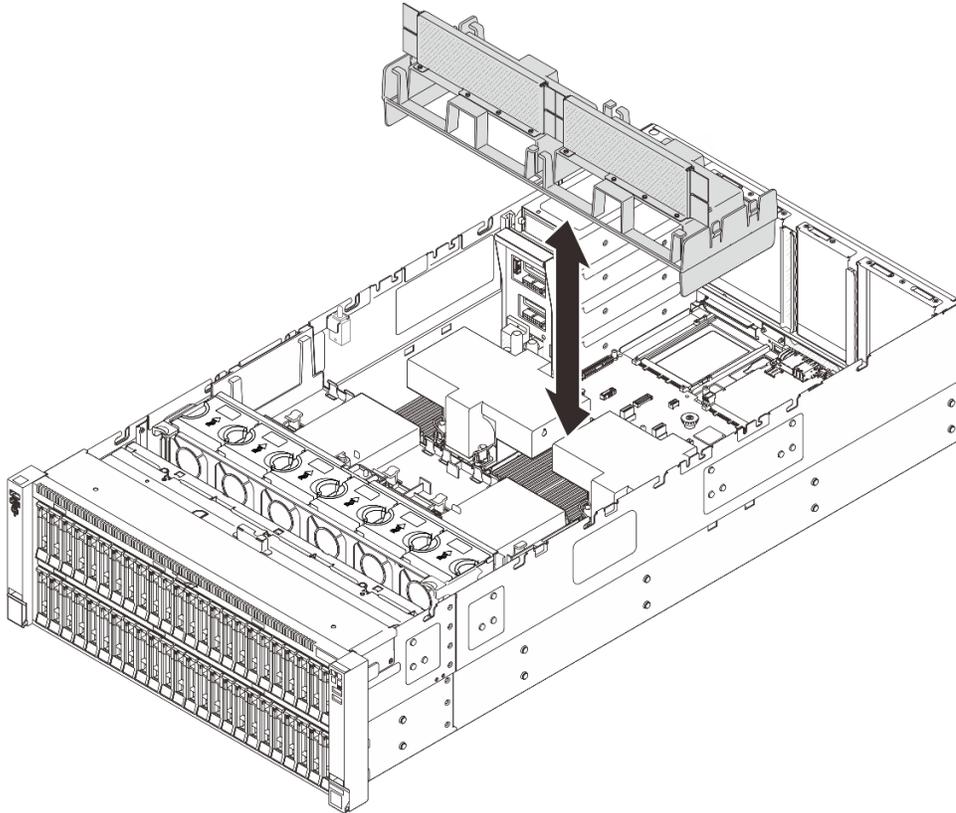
Retrait de la grille d'aération arrière pour un module de processeur-dissipateur thermique 2U de performance
